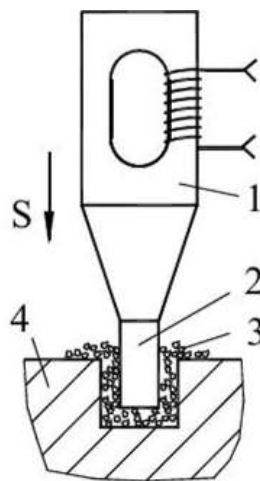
Схема ультразвукової обробки: 1 – перетворювач; 2 – інструмент;
